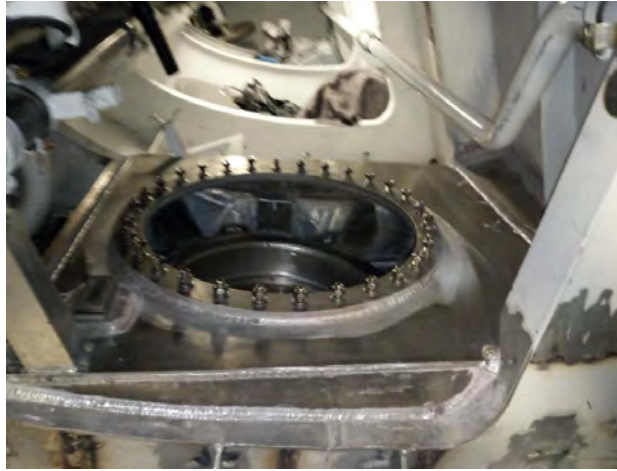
Soldadura plancha principal (Fuente: Trabajo de campo)
